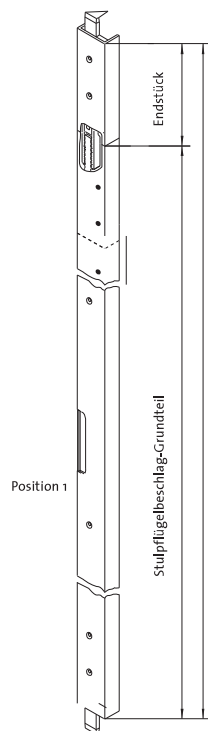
Positionierung (Einbaulage des Stulpflügelbeschlages zum Schließblech
